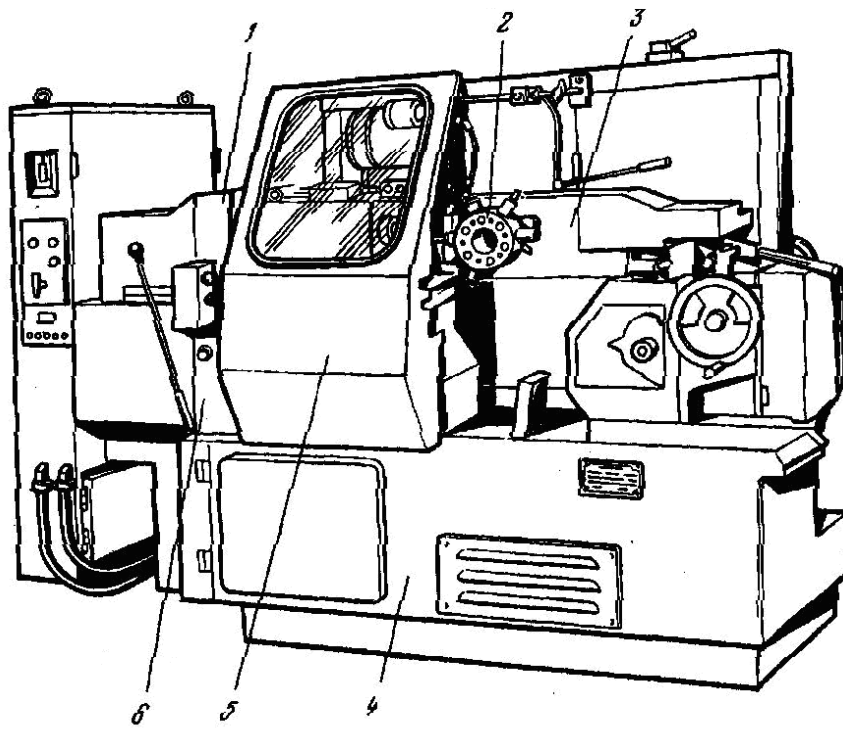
Токарно-револьверний автомат мод. ІЕ140П
